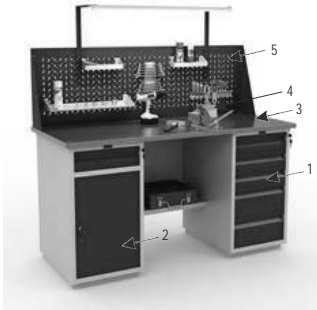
Слюсарний одномісний верстак з поворотними лещатами: 1 – висувні ящики; 2 – тумба; 3 – стільниця; 4 – лещата; 5 – місце для закріплення інструменті
